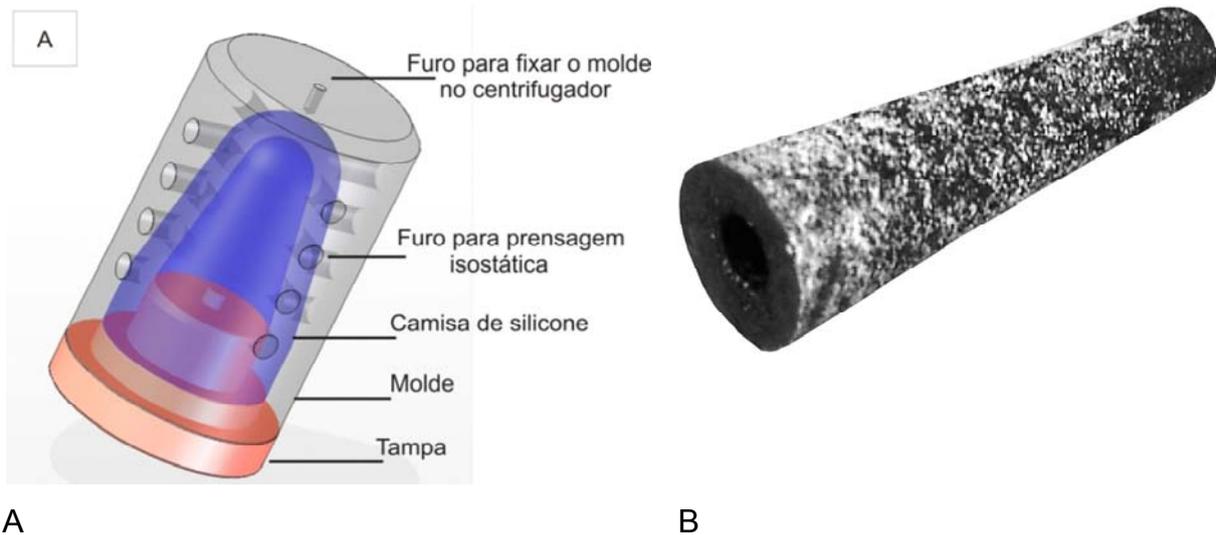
Molde para prensagem isostática do corpo-de-prova. (A) Ilustração do molde; (B) *Blank*, resultado da co-prensagem.
